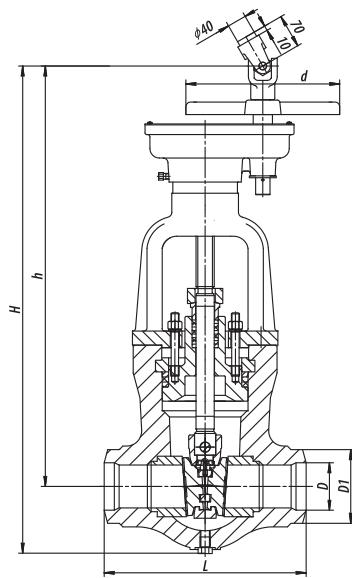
Задвижка DN100 с цилиндрическим редуктором
